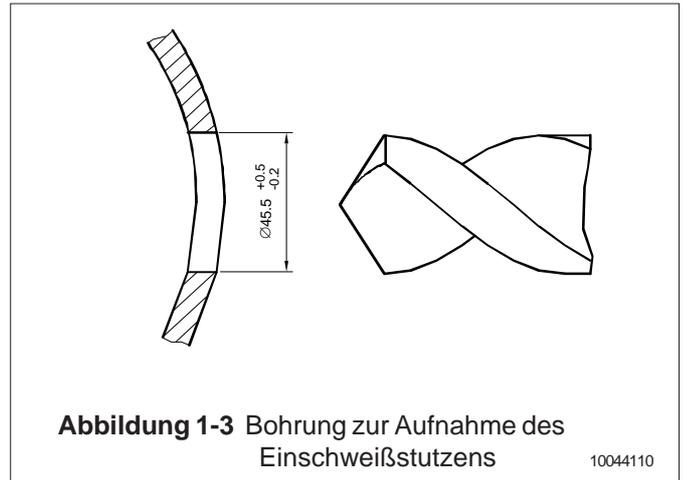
Bohrung zur Aufnahme des Einschweißstutzens
